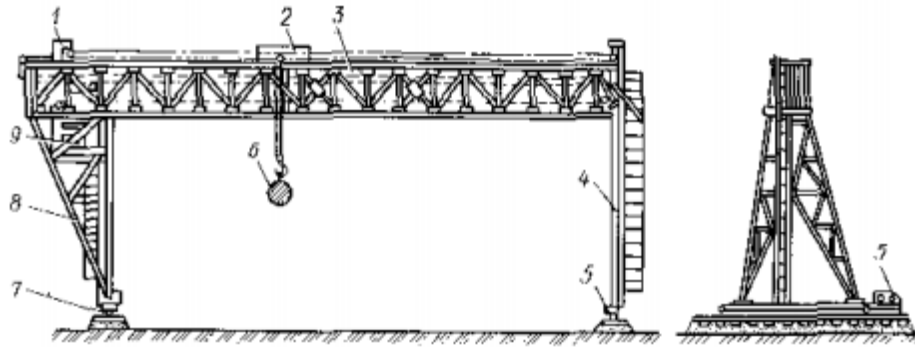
Козловий кран ЛТ-62: Лебідка 1; Вантажний візок 2; Несуча ферма 3; Опори - твердої 8 і 4 шарнірної конструкції; Ходові візки 5 та 7; Вантаж 6; Кабінка кранівника 9;
